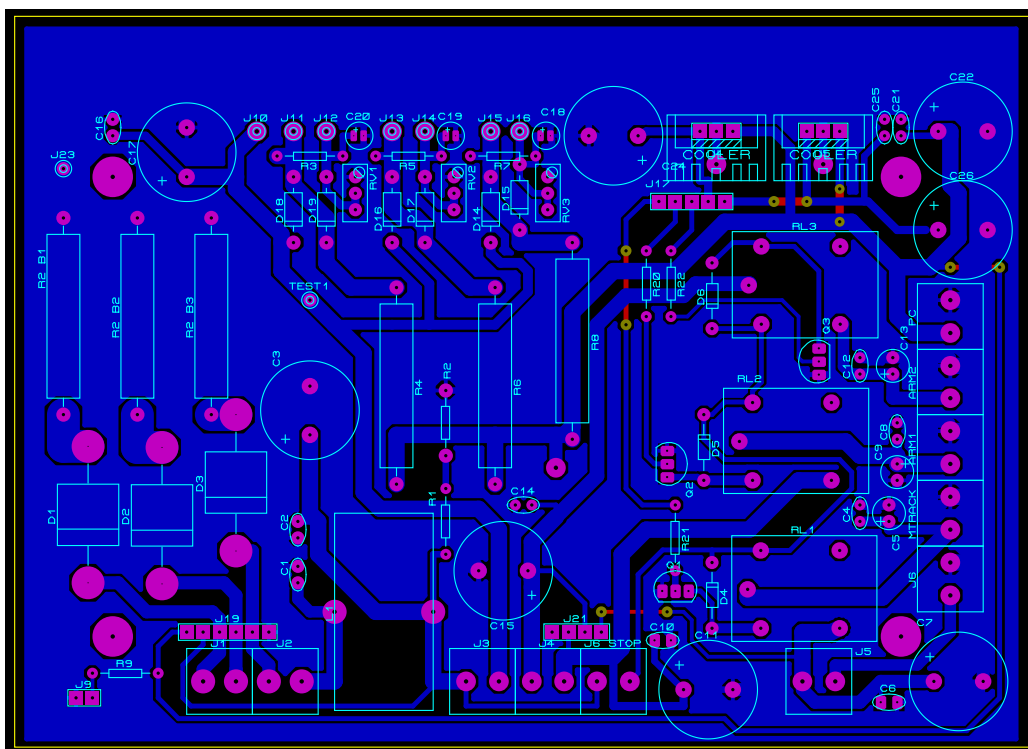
(a) PCB de la Placa de Convertidor DC/DC
